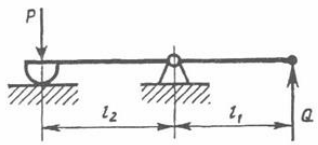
Схема дії важеля першого роду – планки-прихоплювача
